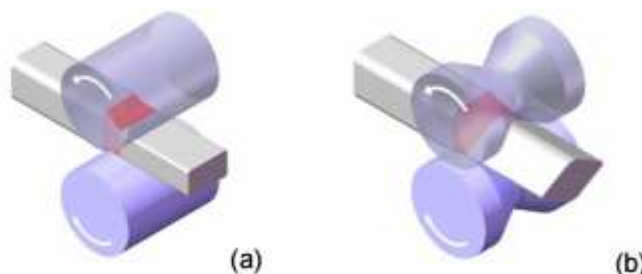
Laminação plana (a) e laminação em canais (b) [4].
